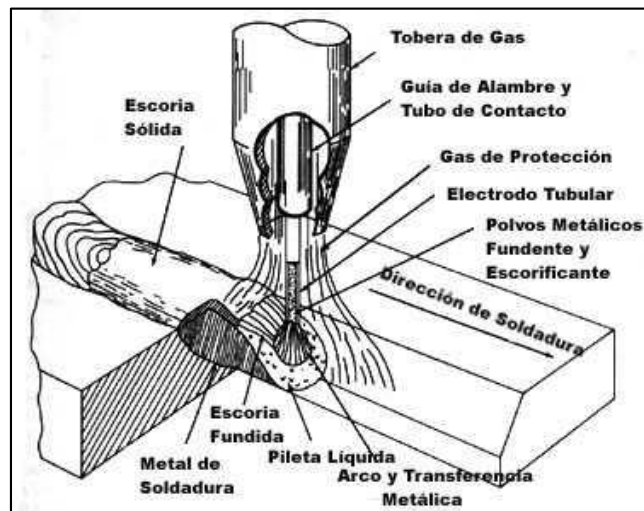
Zonas formadas por la soldadura.
